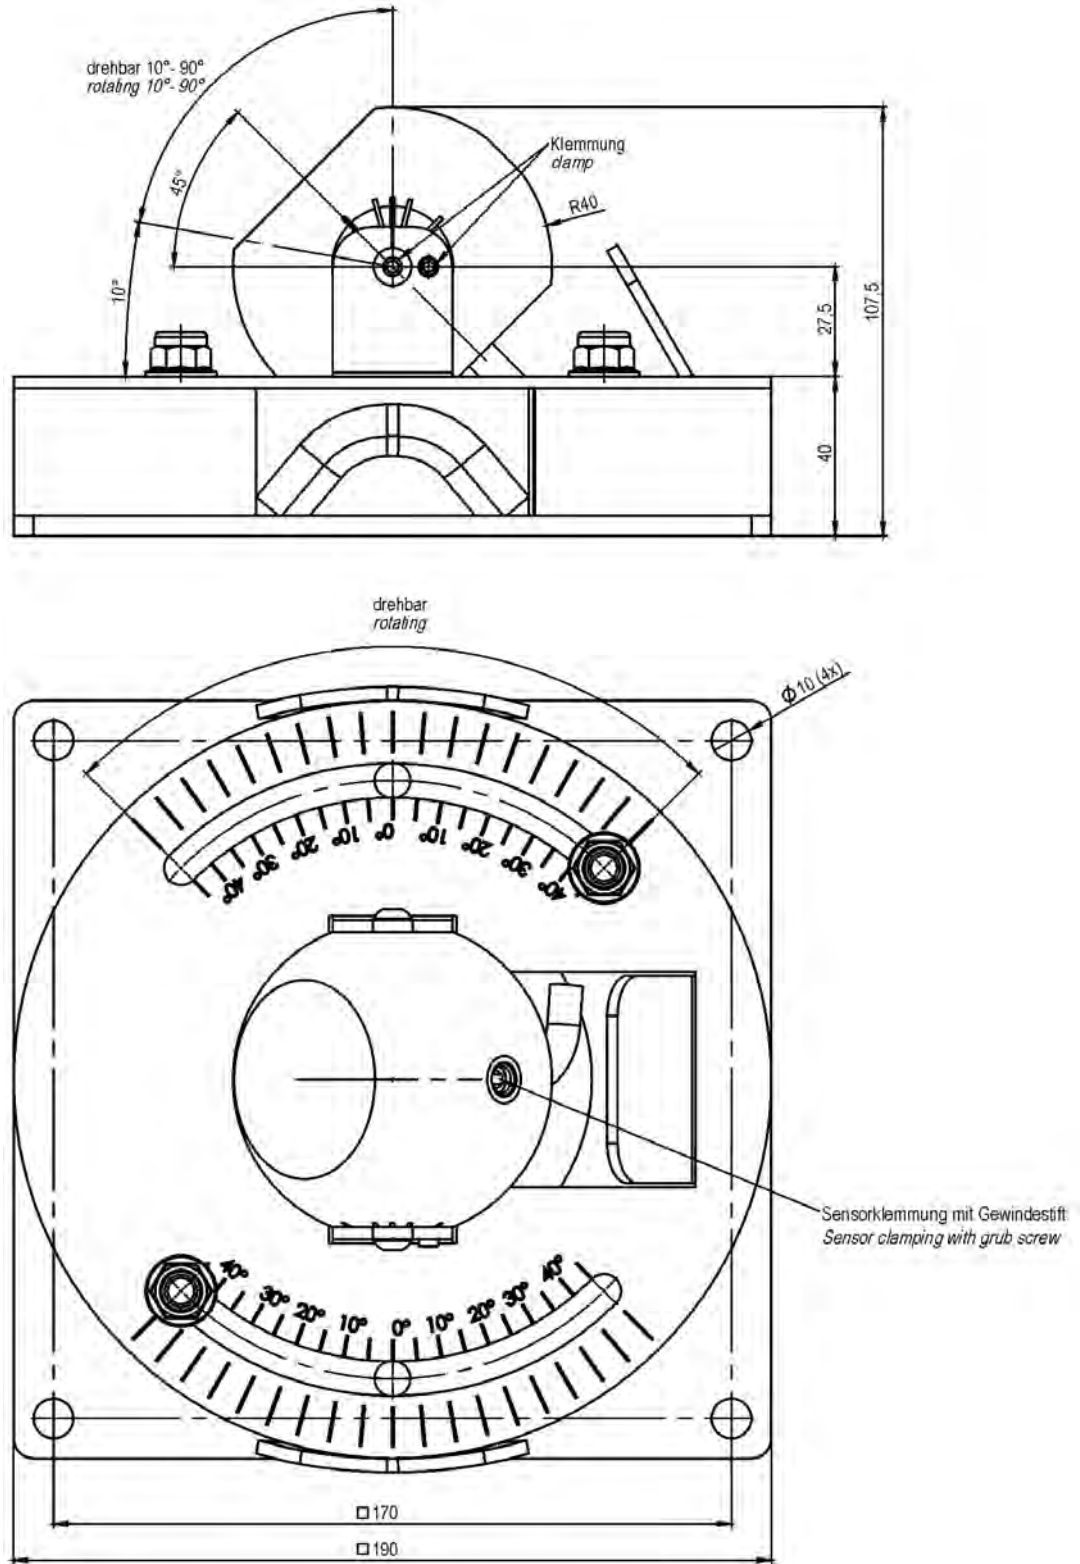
Maßzeichnung Kugelsensor Typ NOS0H0V500
